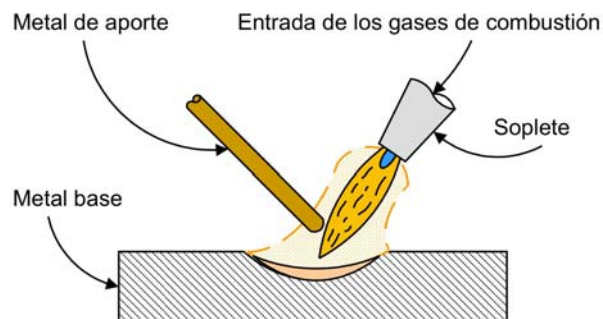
Esquema del proceso de soldadura a tope.
